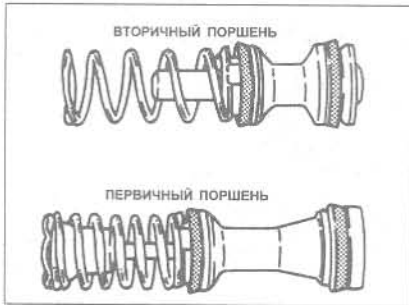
Правильная сборка деталей поршня главного цилиндра (Глава 11)
